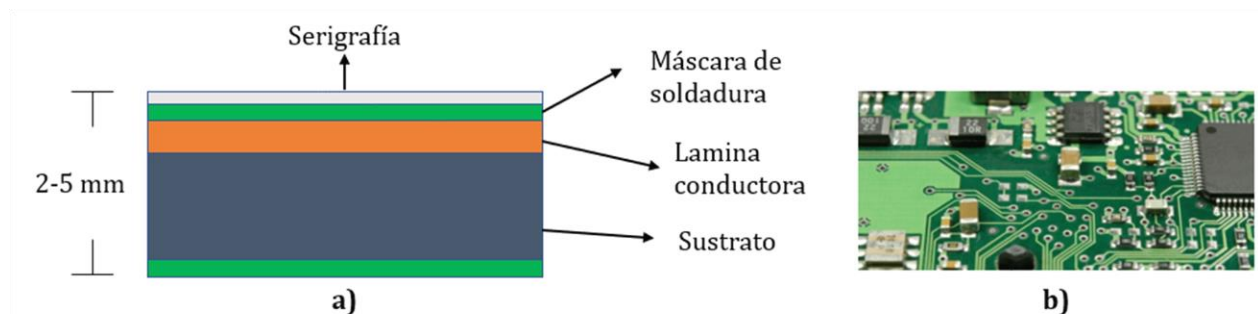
a) Estructura PCB single-layer (adaptado H. Li et al., 2018). b) PCB con componentes electrónicos.
